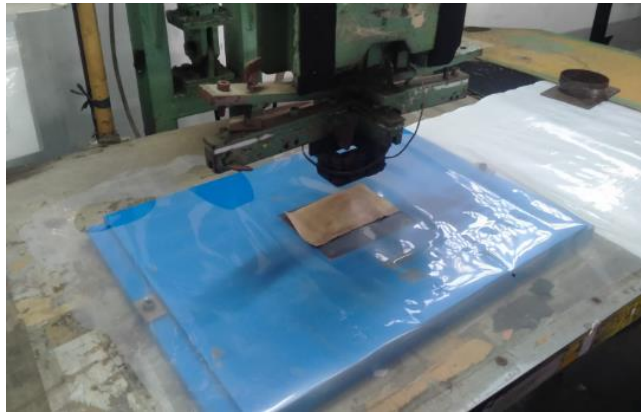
Peletakkan *Sub Sheet Green* Pada *Pola Jig Assy Welder
